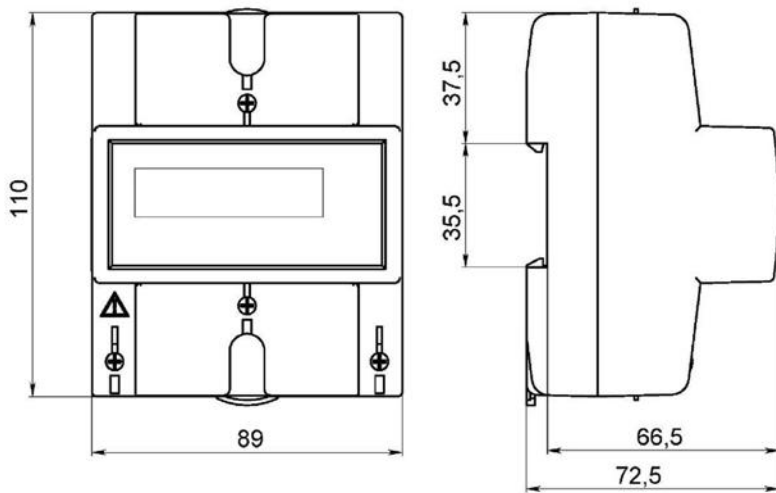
Габаритные и установочные размеры счетчика в корпусе R5
